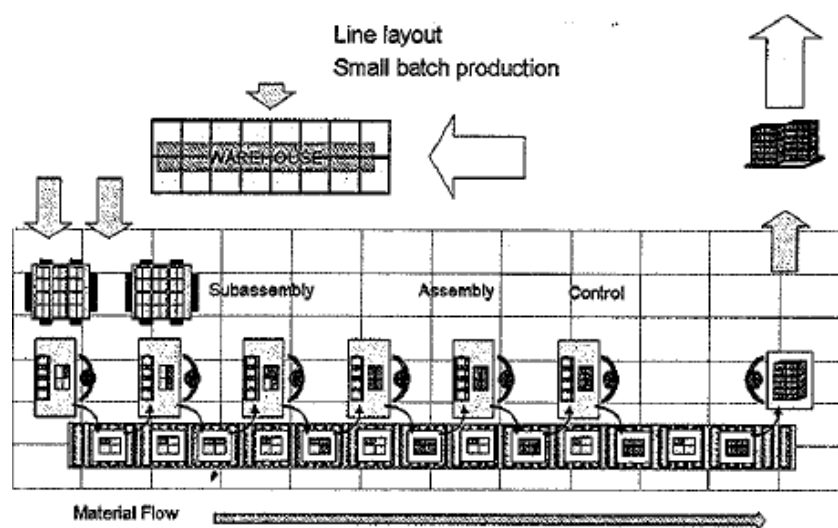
Layout orientado ao produto (Coimbra, 2009)
